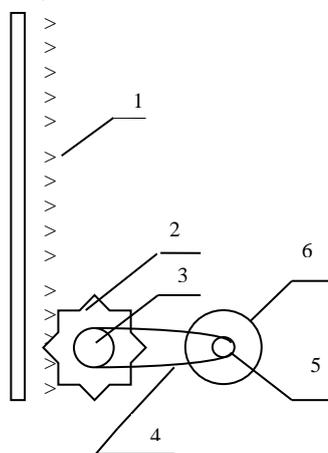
Кинематическая схема механизма автоматической подачи семян: 1 – рейка зубчатая; 2 – шестерня реечная; 3 – шкив ведомый; 4 – ременная передача; 5 – шкив ведущий; 6 – электродвигатель
